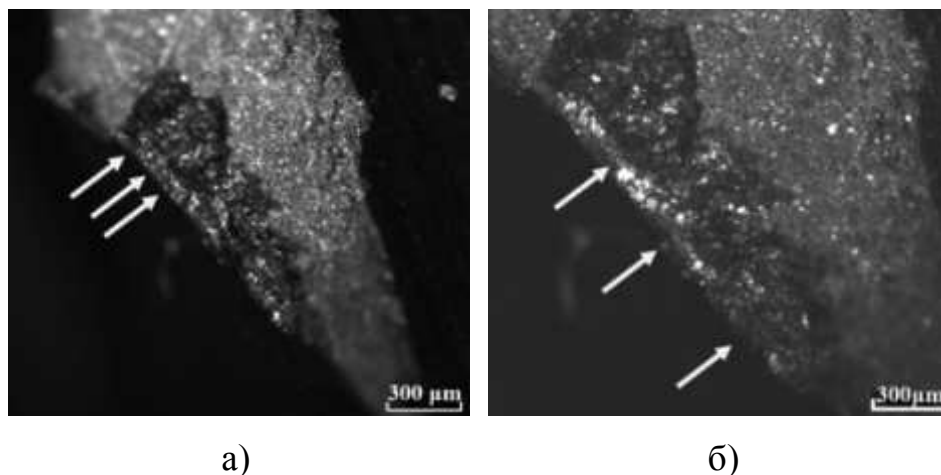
Злам 1. Поверхня зовнішньої обойми підшипника № 7 (оптичний мікроскоп)
